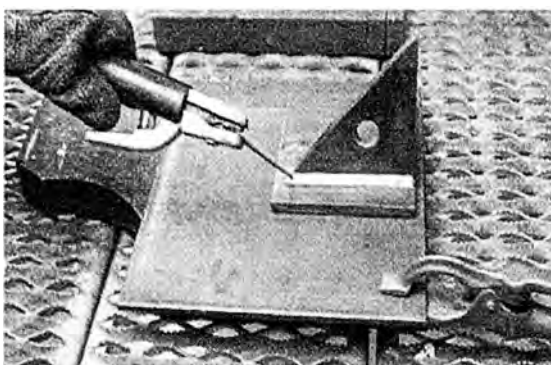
Soldadura por Arco con Electrodo Revestido
